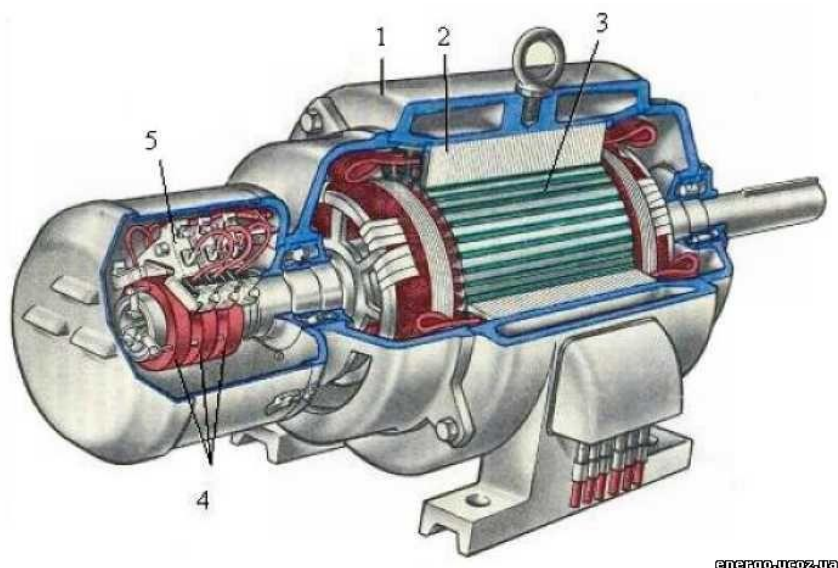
Асинхронный двигатель с фазным ротором в разрезе:
